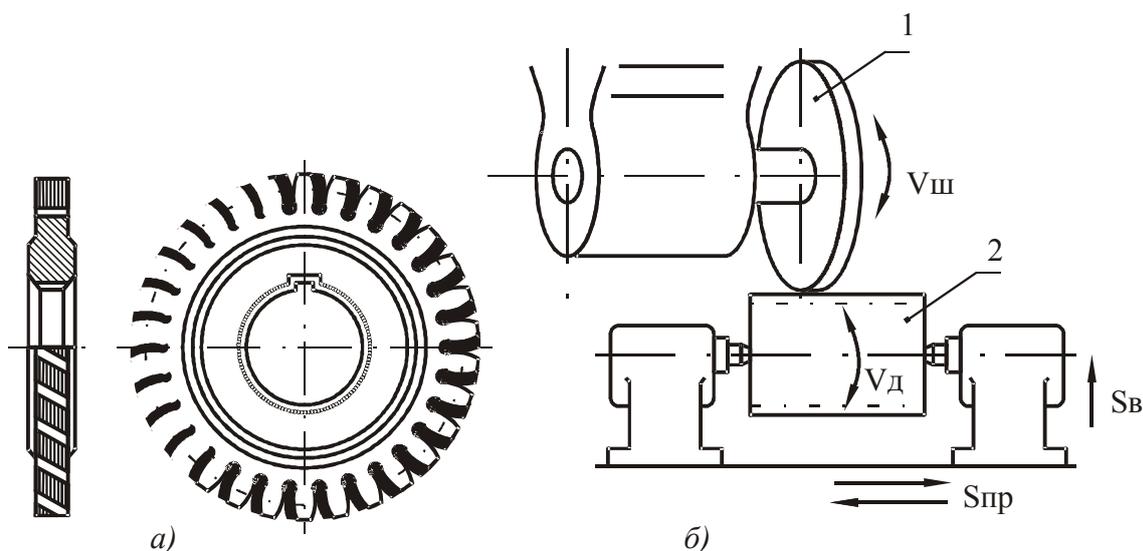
Шевингование: *а* – дисковый шевер; *б* – схема обработки зубьев колес дисковым шевером: 1 – дисковый шевер; 2 – заготовка; $v_{ш}$ – скорость шевера; $v_{д}$ – скорость заготовки; $S_{пр}$ – продольная подача (с реверсированием) стола; $S_{в}$ – вертикальная подача стола
